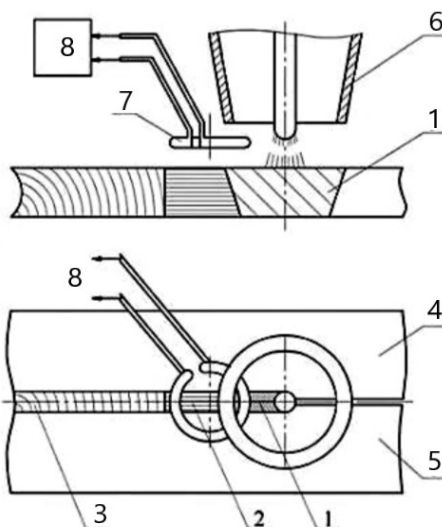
Технологическая система воздействия МИО на расплав сварного шва: 1 – зона расплавления соединяемых металлов; 2 – зона затвердевания металла; 3 – зона полного затвердевания металла; 4, 5 – свариваемые элементы; 6 – сварочная головка; 7 – индуктор; 8 – генератор магнитных импульсов
